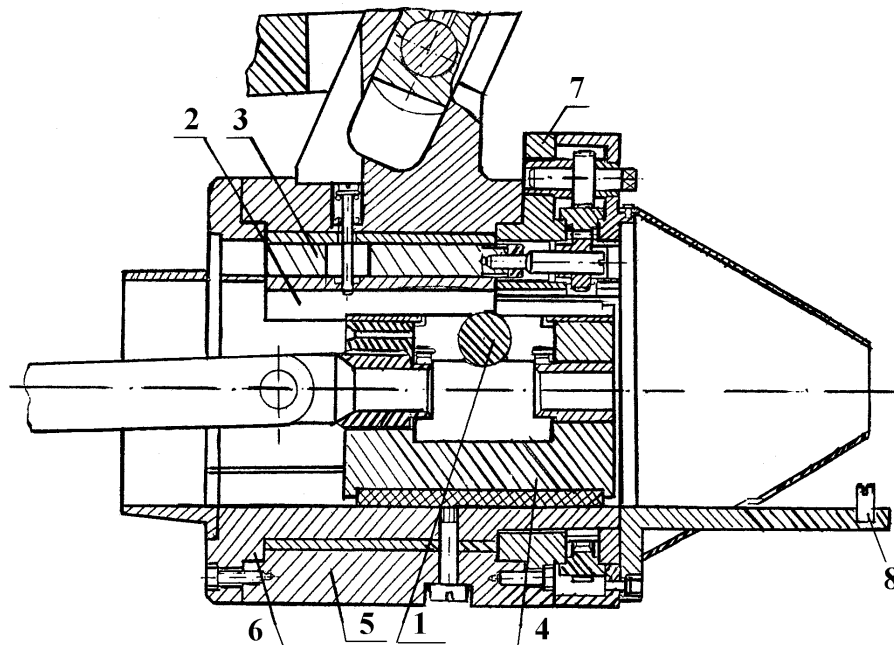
Робоча кліть стану ХПТР 15 - 30 конструкції заводу важкого машинобудування: 1 - ролик; 2 - планка; 3 - клин; 4 - повзун; 5 - корпус; 6 - фіксуюча труба; 7 - механізм пересування клинів; 8 - обмежник.
